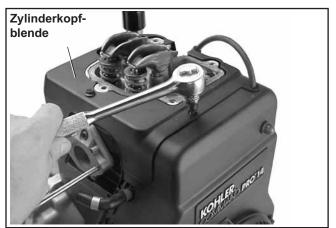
Ausbau der Zylinderkopfblende.
